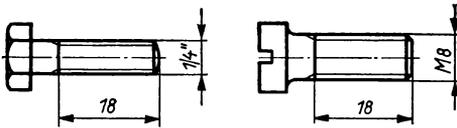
Bezeichnung der Gewinde und Angabe der Gewindelänge
